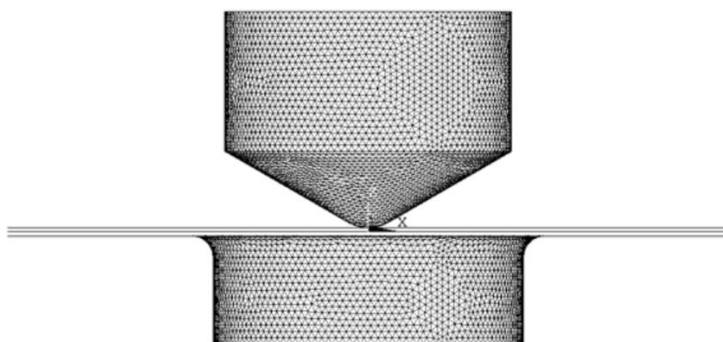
Конечно-элементная сетка инструмента и заготовки
